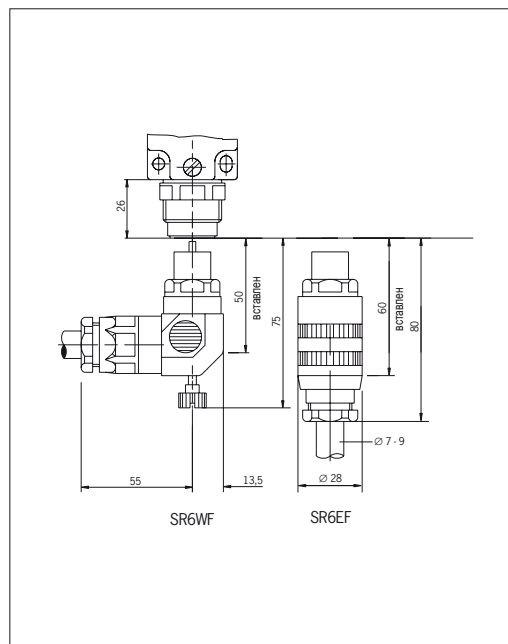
Чертеж с размерами NG2... со штекерным соединителем SR6
